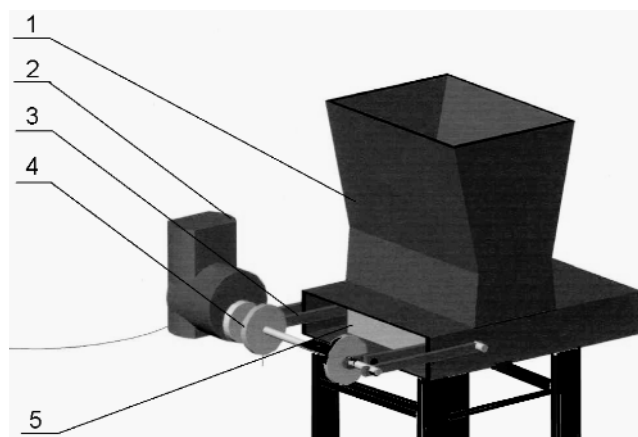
Специальная установка для устройства подливки под оборудование с высоким фундаментом :
